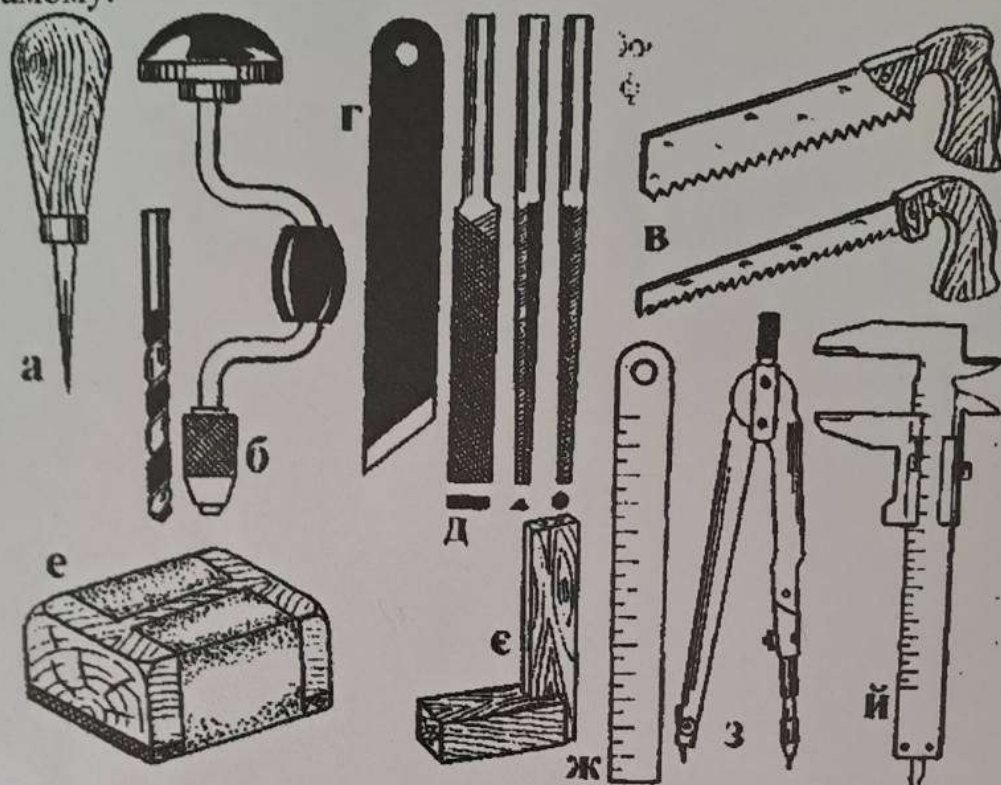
Інструменти та пристрої, що використовуються при випилюванні: а — шил; б — коловорот з свердлом; в — ножівки; г — ніж шевський; д — напилки або надфіли; е — шліфувальний брусок; е — кутник столярний; ж — лінійка; з — циркуль учнівський; й — штангель циркуль
